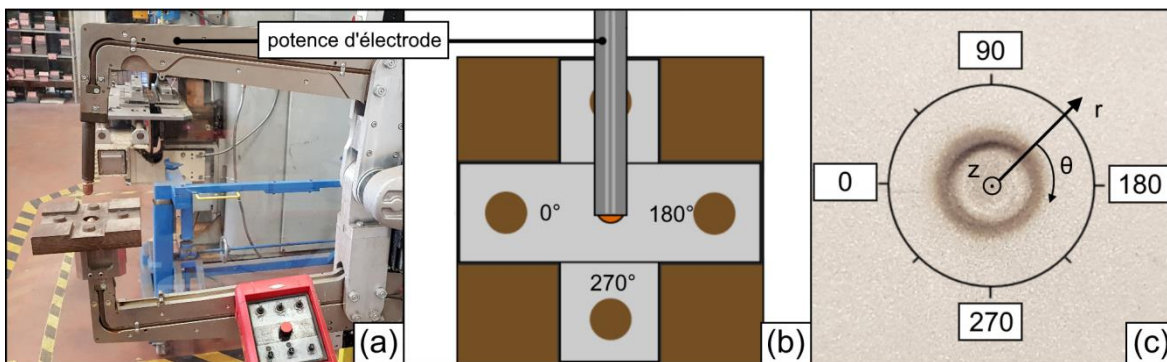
(a) Machine de soudage vue de côté ; (b) Schéma en vue du dessus avec indication du repère angulaire azimutal ; (c) Photo d'une soudure vue du dessus
